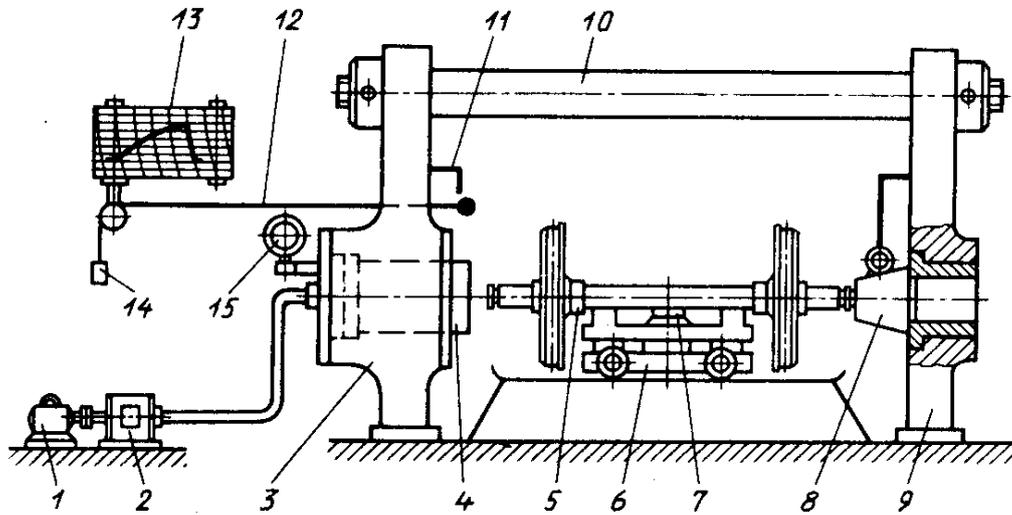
Схема гидравлического пресса для формирования колесных пар: 1 – электродвигатель; 2 – насос; 3 и 9 – соответственно передняя и задняя стойки пресса; 4 – плунжер; 5 – колесная пара; 6 – тележка для установки колесной пары; 7 – пневматический выталкиватель; 8 – откидная опора для второго перехода прессования; 10 – траверса пресса; 11 – откидной упор для первого перехода прессования; 12 – тросик индикатора; 13 – индикатор; 14 – груз тросика; 15 – манометр
